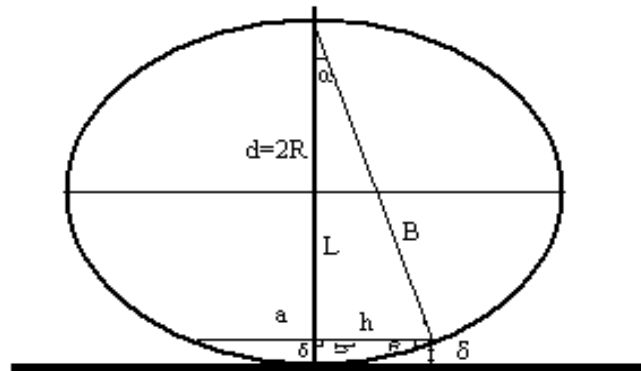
Розрахункова схема радіуса заокруглення вертикальної робочої поверхні фрикційного клину
